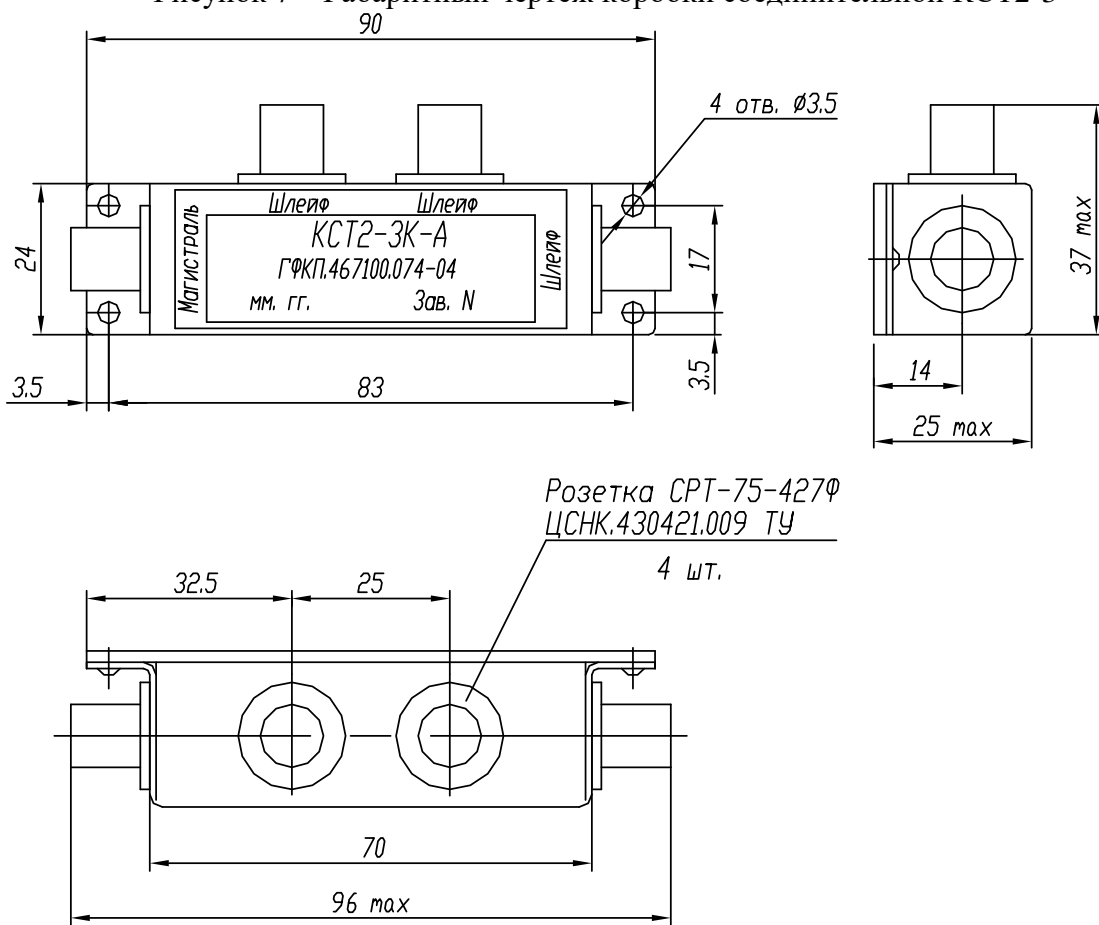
Габаритный чертеж коробки соединительной КСТ2-3К
